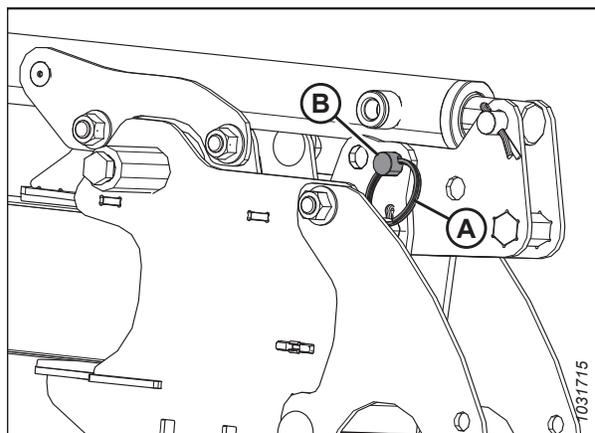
Cilindro del braccio destro – Posizione avanzata
